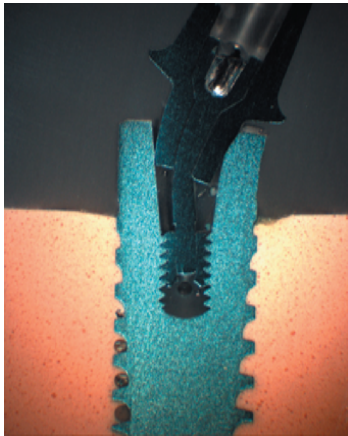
Querschnitt eines Implantates mit Abutment nach Belastungstest. Deutliche Deformationen im Bereich der Abutmentschraube und des Abutmenthalses.
